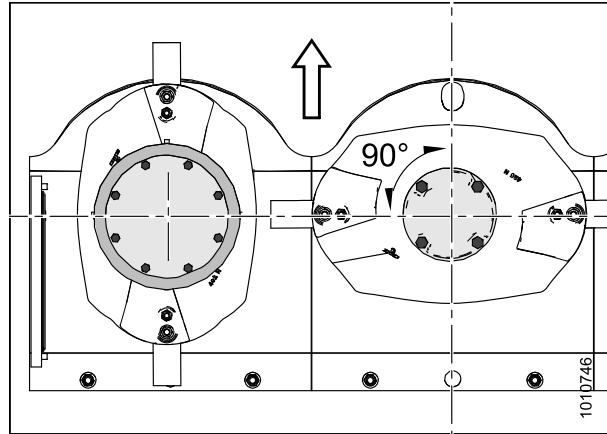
Disques de la barre de coupe (vue de dessus)
